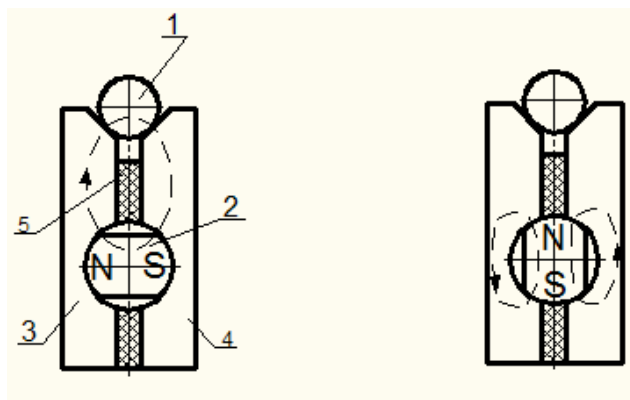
Схема приспособления с постоянным магнитом: а – закреплено, б – откреплено.
